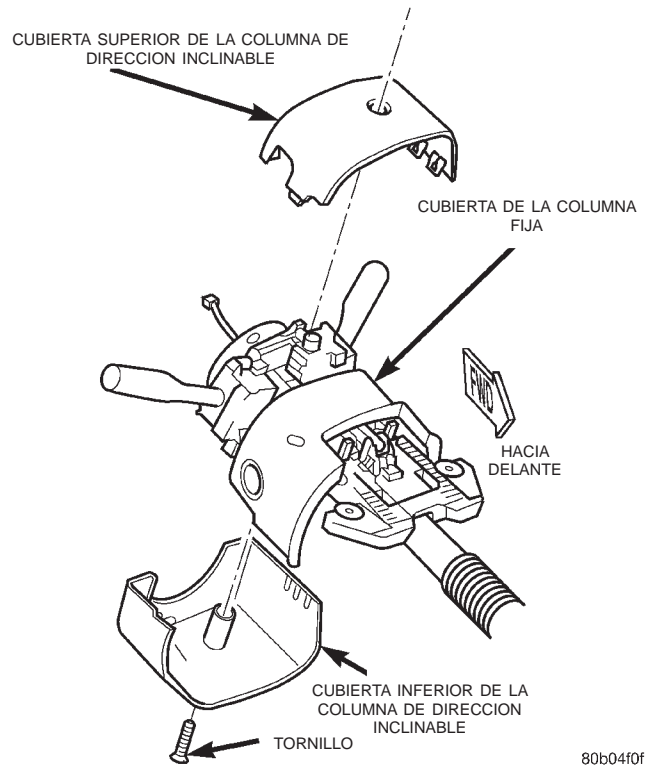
Desmontaje e instalación de las cubiertas de la columna de dirección
